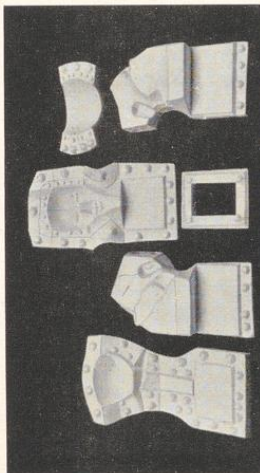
Die Keilstücke sind in die zugehörigen Mantelteile eingelegt
